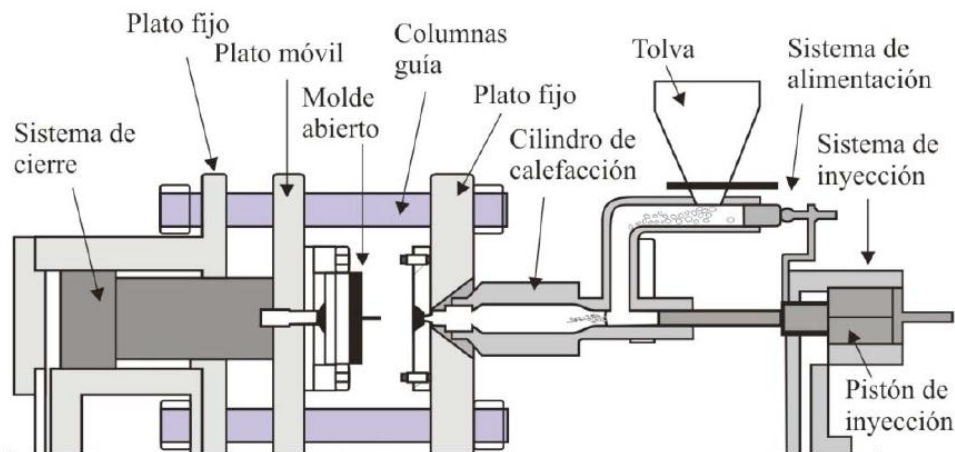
Esquema de la máquina de moldeo por inyección con pistón.
